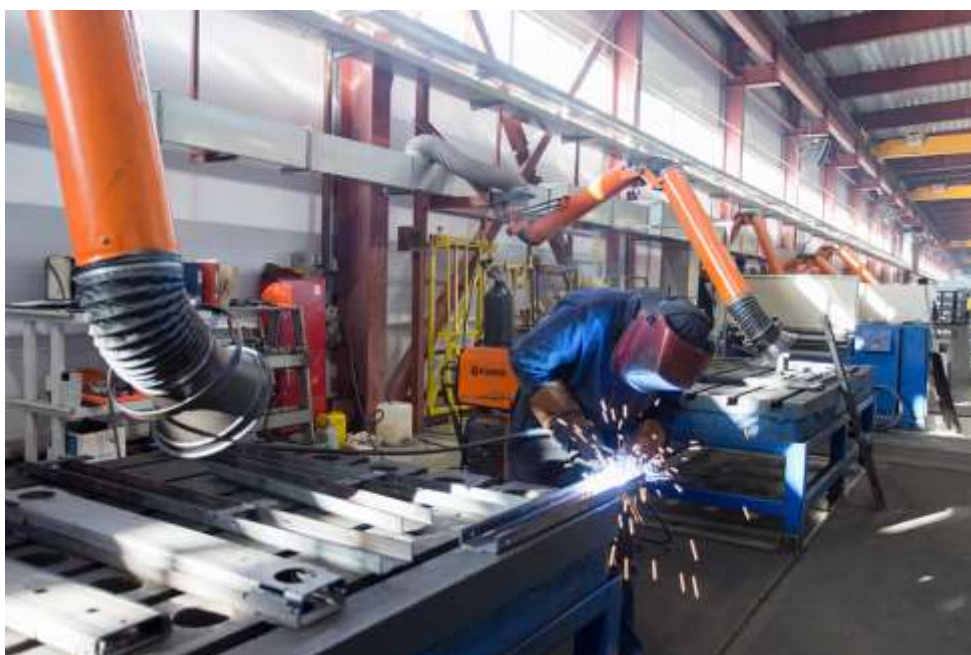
Сварочное оборудование «LINCOLN»
